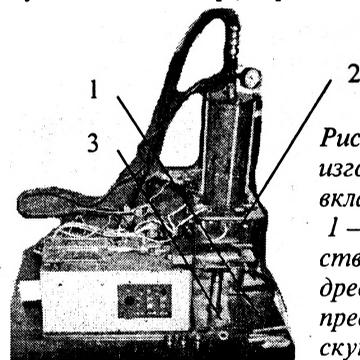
Полуавтомат для изготовления древесного вкладыша:
